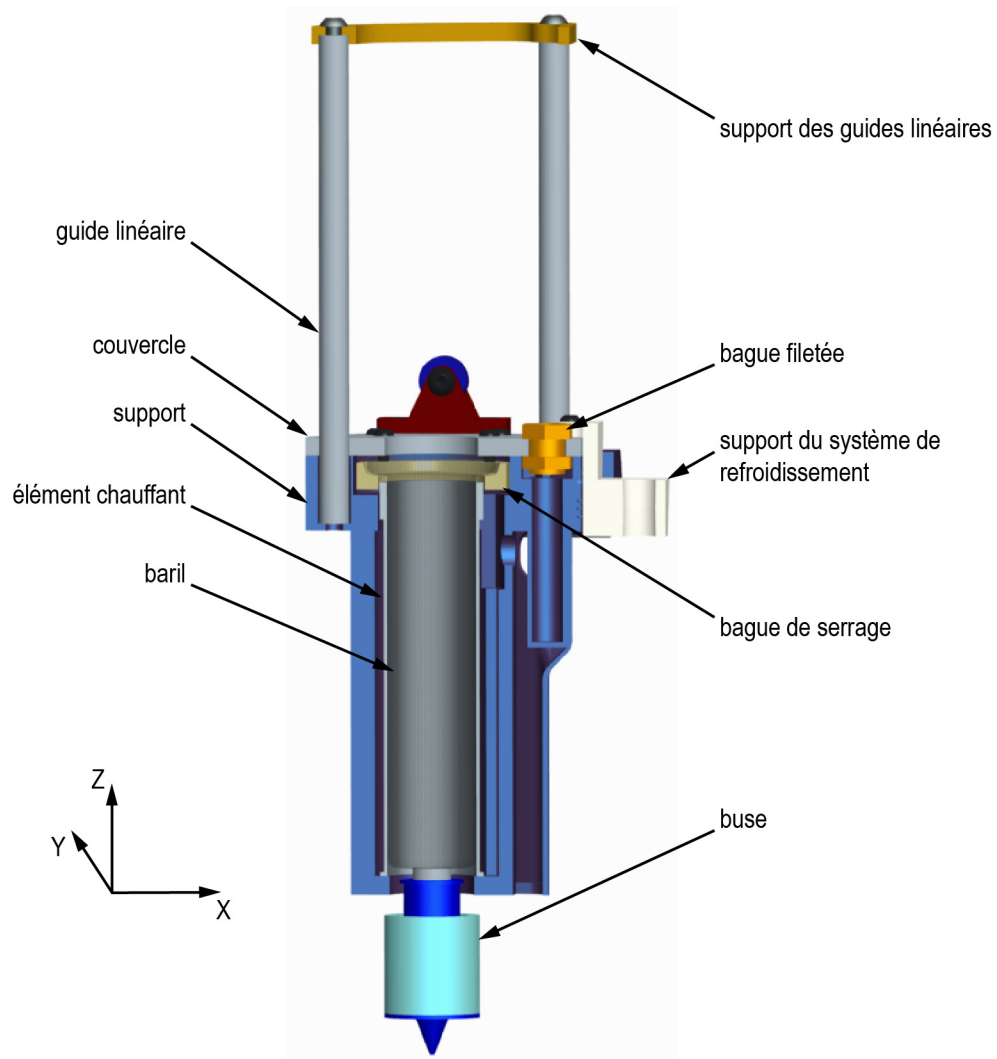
Vue de coupe du sous-ensemble du corps de la tête d'impression.
